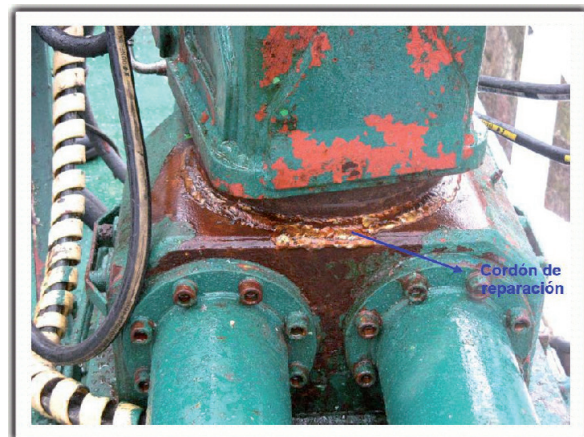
Cordón de soldadura en la base de la grúa.
